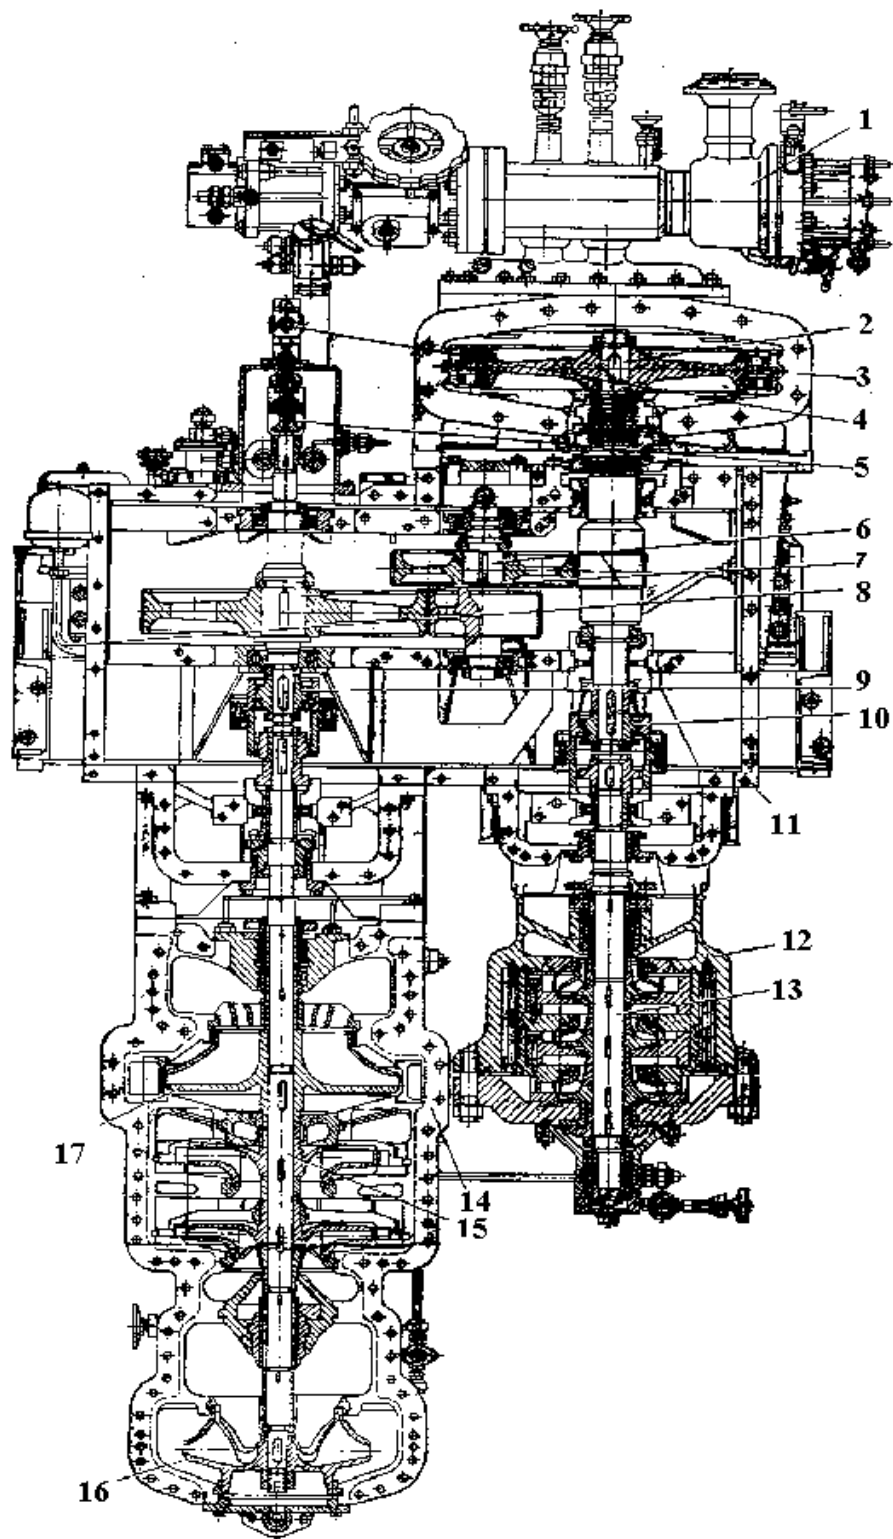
Общий вид ПКБТ со снятыми крышками корпусов:
